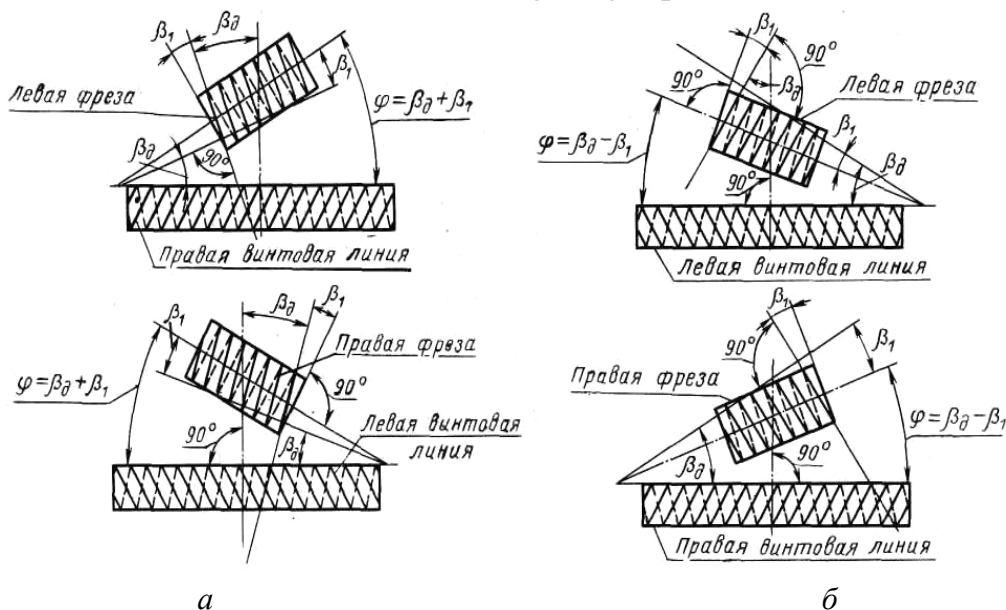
Взаимное расположение червячной фрезы и заготовки при нарезании цилиндрического колеса с винтовой нарезкой
